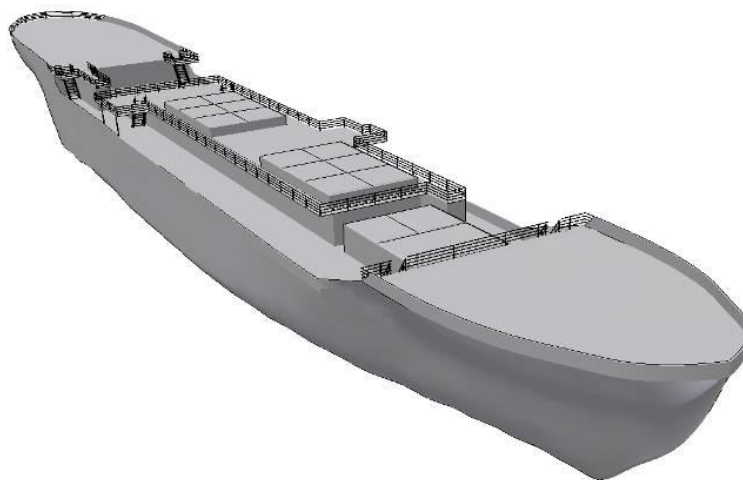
Общий вид блока-упаковки в виде цельного корпуса судна
